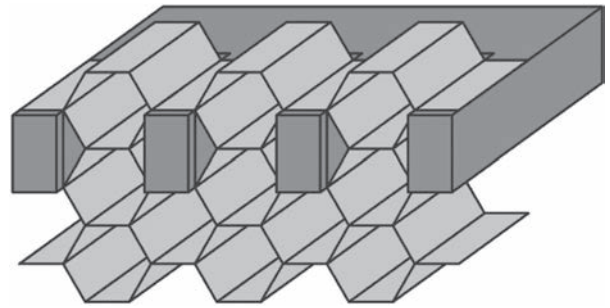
Вид оснастки «гребенка» для сварки сотового заполнителя
